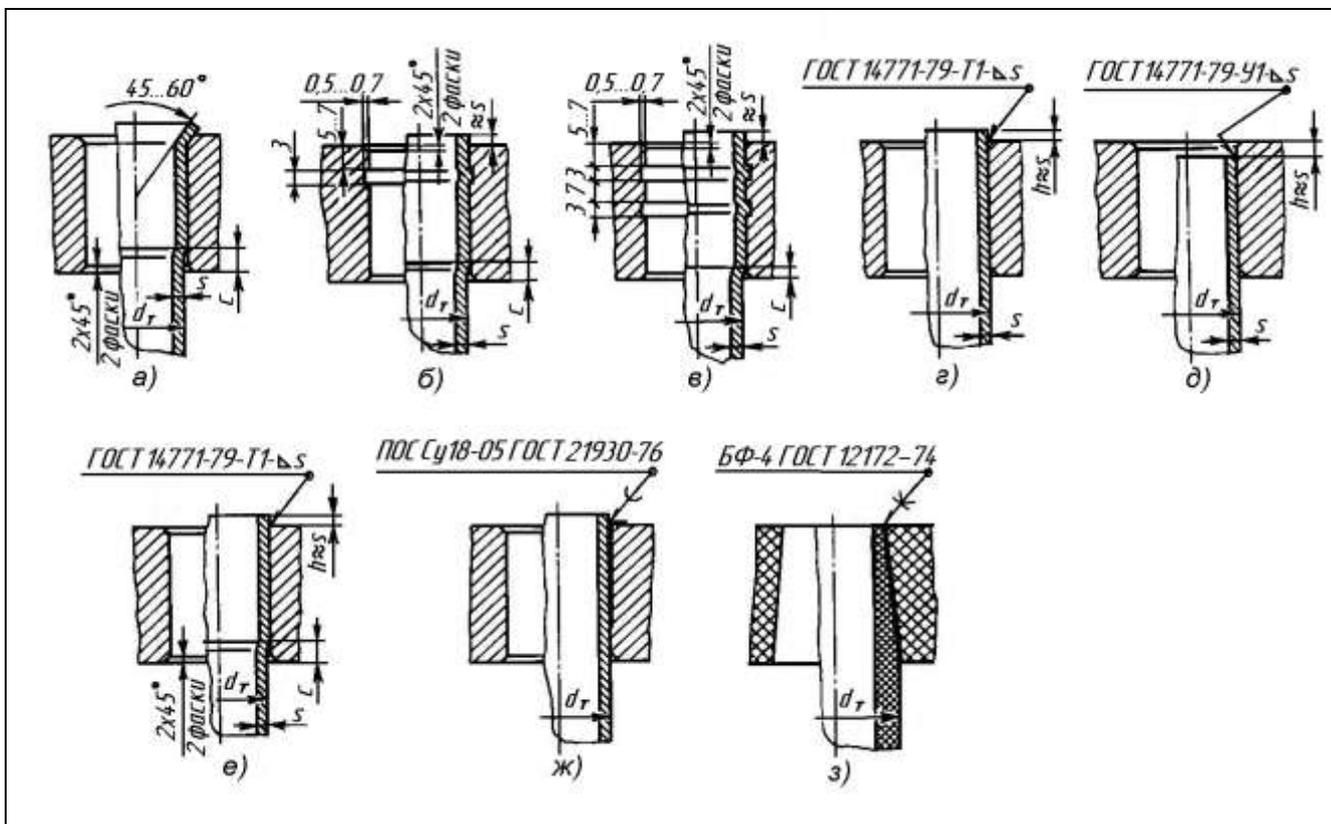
Способы соединения труб с трубной решеткой: а) – развальцовка в гладких отверстиях с разбортовкой; б), в) – развальцовка в отверстиях с одной и двумя канавками соответственно; г), д) – сварка выступающих и утопленных концов труб; е) – сварка с развальцовкой; ж) – пайка; з) – склеивание
